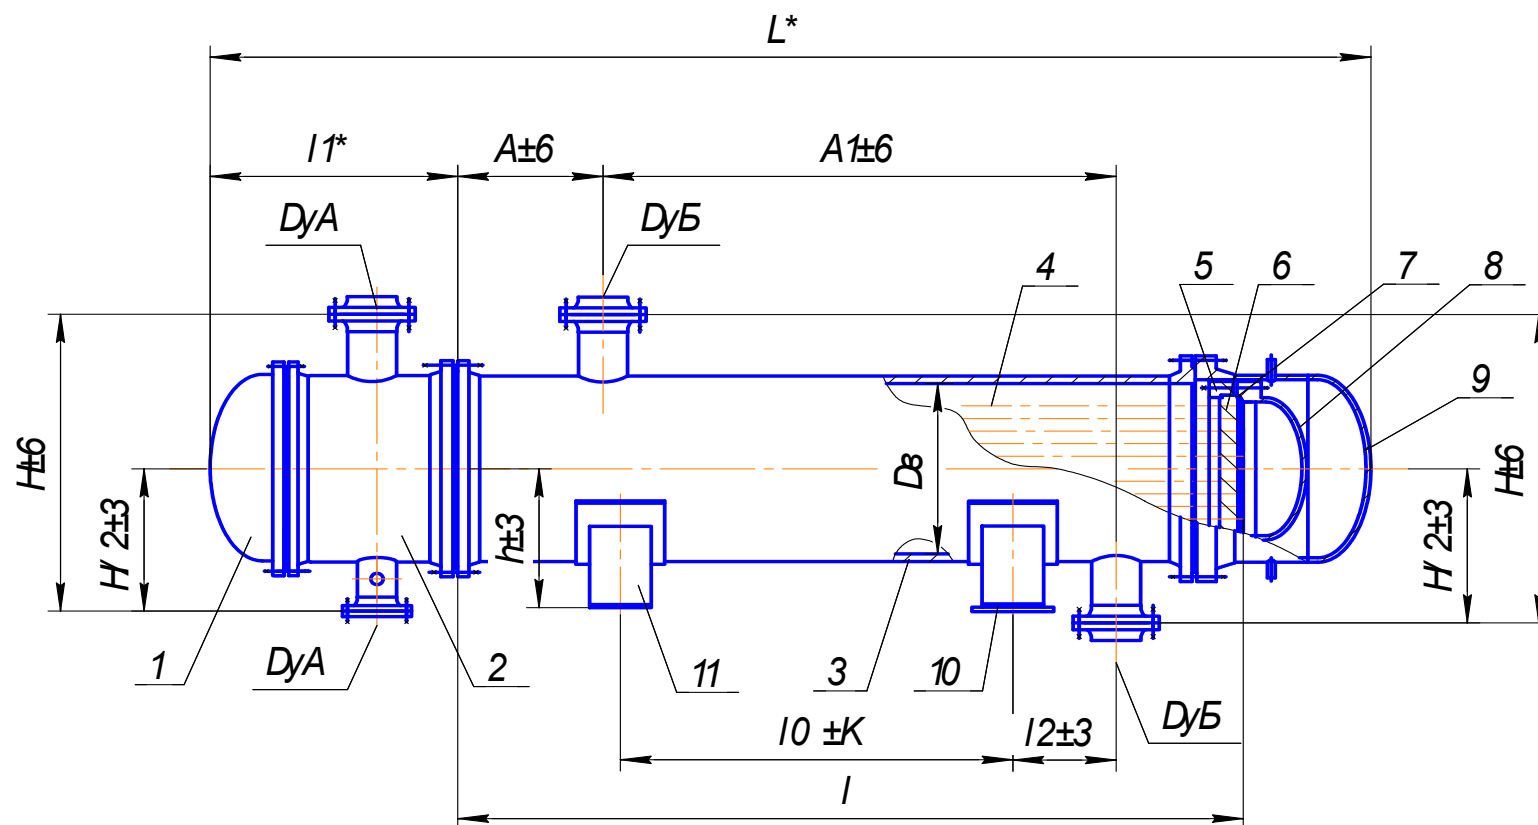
Аппарат типа ТПГ. 1 – крышка камера распределительной; 2 – камера распределительная; 3 – кожух; 4 – труба теплообменная; 5 – полукольцо; 6 – решетка трубная подвижная; 7 – прокладка плавающей головки; 8 – крышка плавающей головки; 9 – крышка кожуха; 10 – опора подвижная; 11 – опора неподвижная.
